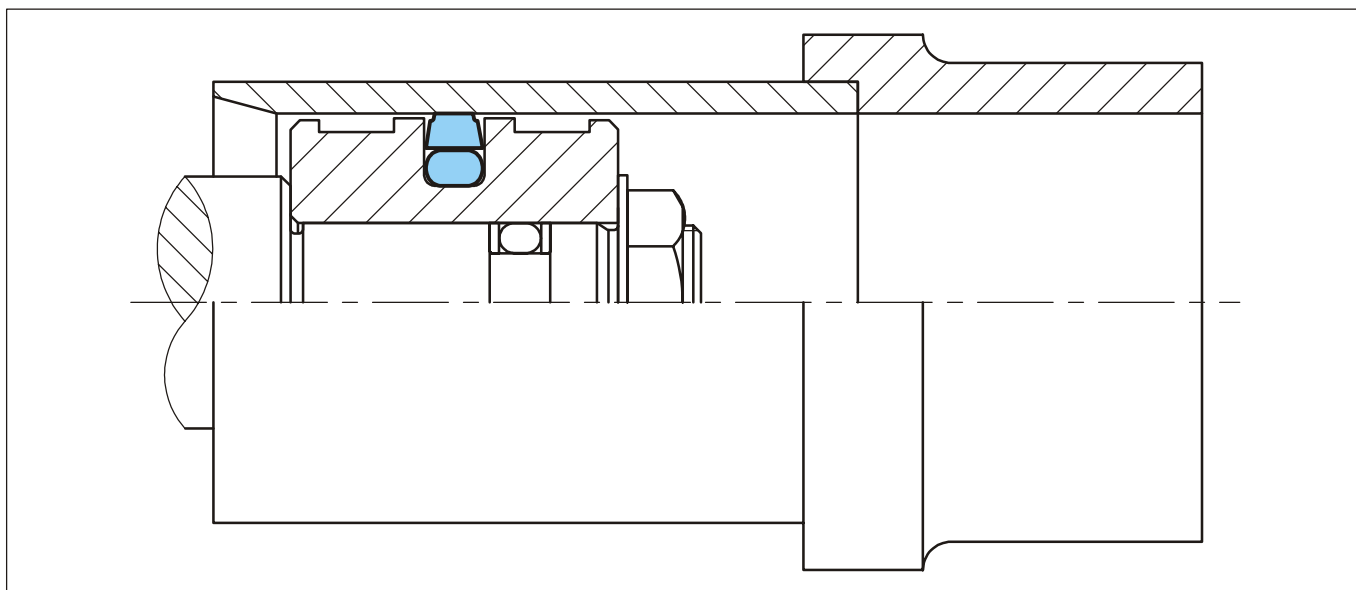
Калибровка уплотнительного элемента калибрующей втулкой
